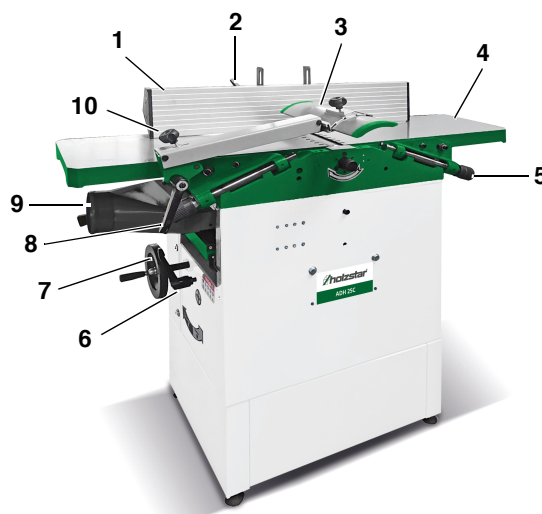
Abricht- und Dickenhobelmaschine ADH 25 C
